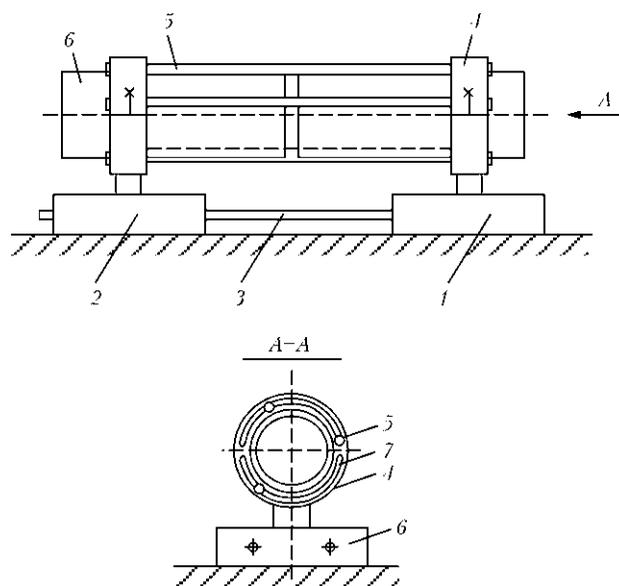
Схема устройства для сварки труб из термопластов (обозначения см. в тексте)
